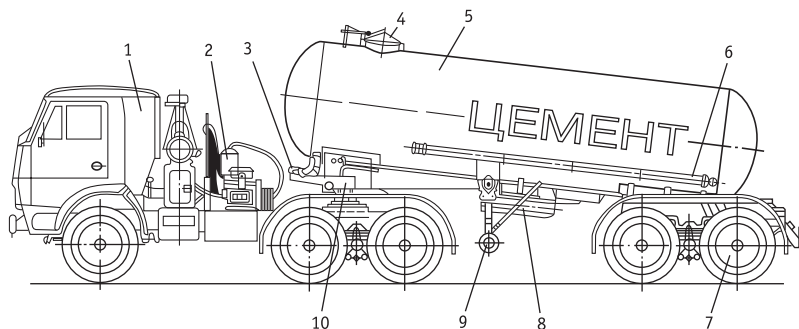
Автоцементовоз ТЦ-11: 1 – седельный тягач КамАЗ-5410; 2 – компрессорная установка; 3 – пневмооборудование для разгрузки; 4 – загрузочный люк; 5 – цистерна-полуприцеп; 6 – разгрузочный рукав; 7 – ходовая часть; 8 – запасное колесо; 9 – опорное устройство; 10 – сцепное устройство.
